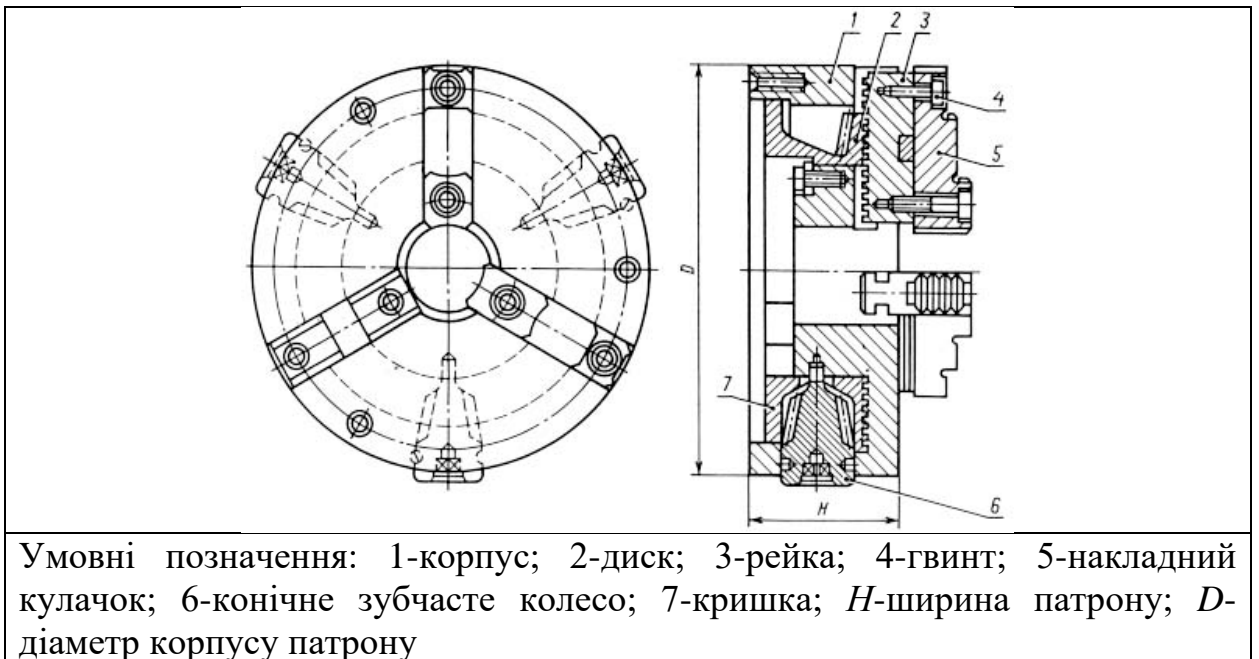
Трикулачковий самоцентрувальний патрон з ручним закріпленням заготовки
